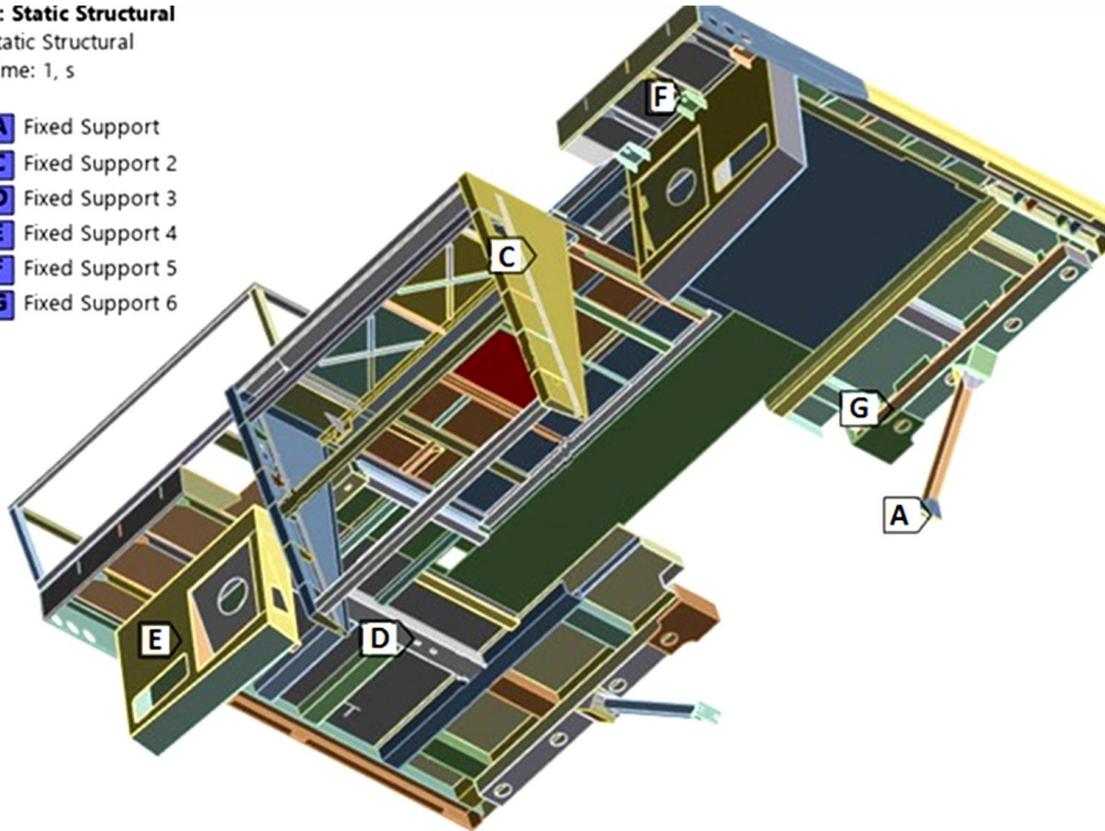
Расчетная схема палубы карьерного самосвала БелАЗ-75131 (места закрепления палубы - вид снизу)
